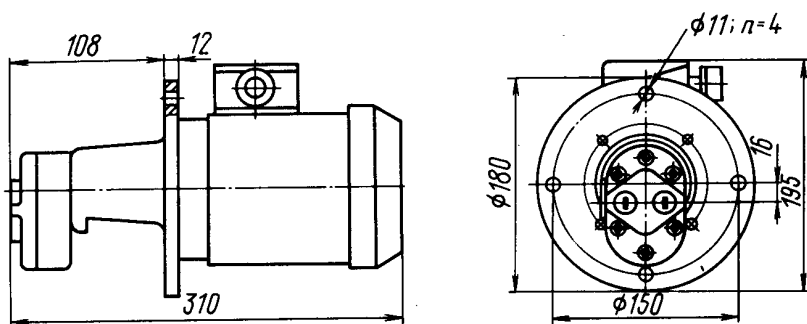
Габаритные и присоединительные размеры агрегата типа ВГ11-1 с двигателем серии АИР63А4
